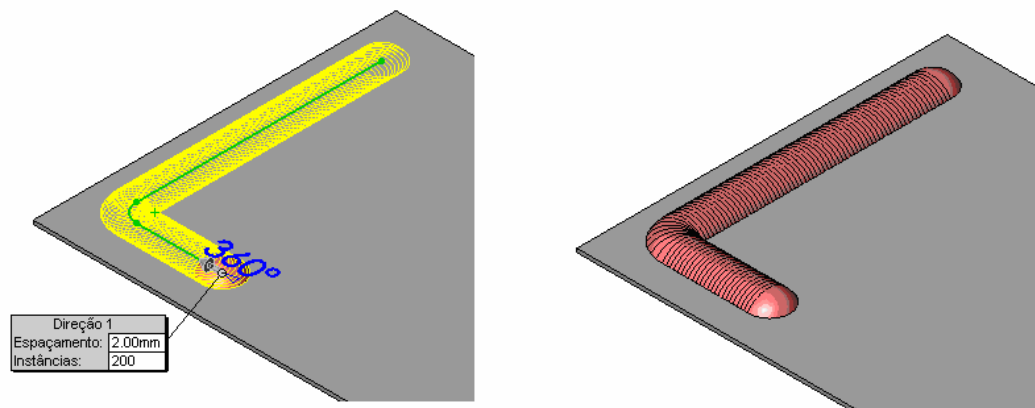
Sobreposição de calotas esféricas formando um cordão de solda.
